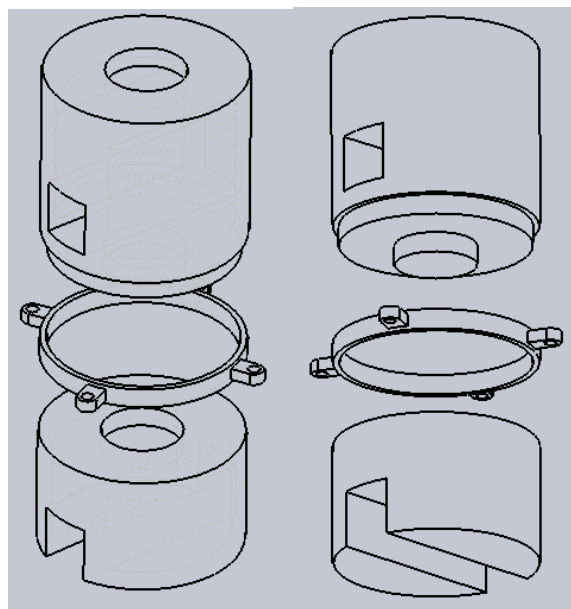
Vista explodida do sistema de 2 cilindros com o aro
